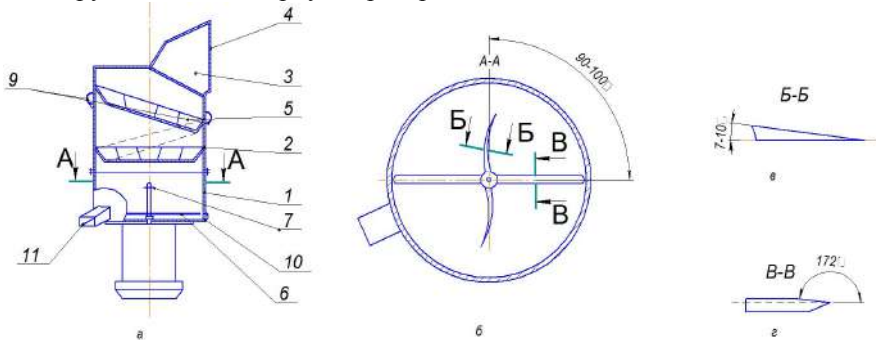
Конструкція ножової дробарки а – загальний вигляд; б – розташування ножів в корпусі дробарки; в – кут загострення серпоподібних ножів; г – кут загострення клиноподібних ножів
